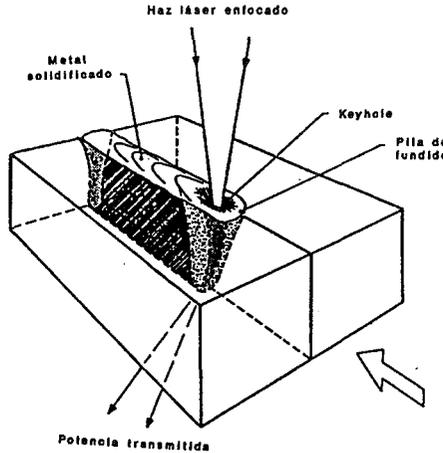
Representación esquemática del proceso de soldadura con láser
